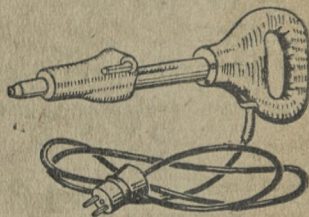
Нагревательный инструмент для взрывных заклёпок
